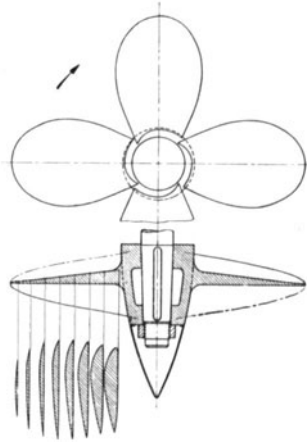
Schema einer Schiffsschraube (Schnelldampfer „Bremen“).
